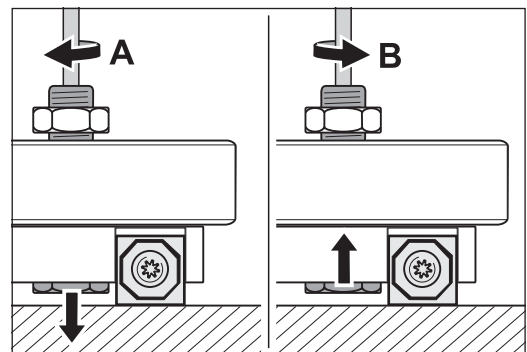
Die Einstellschraube nach unten (A) oder nach oben (B) drehen.
